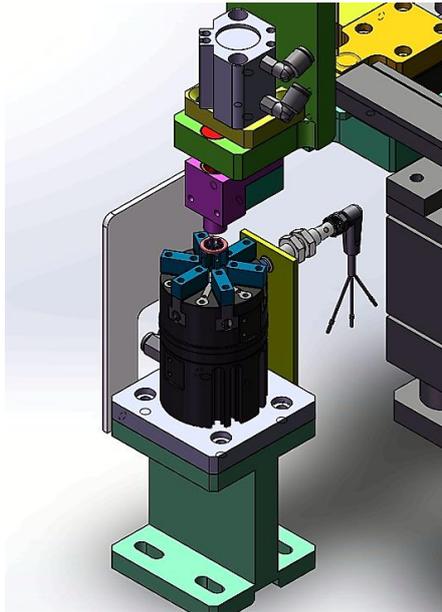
Conjunto colocación de junta. Fuente:propia
